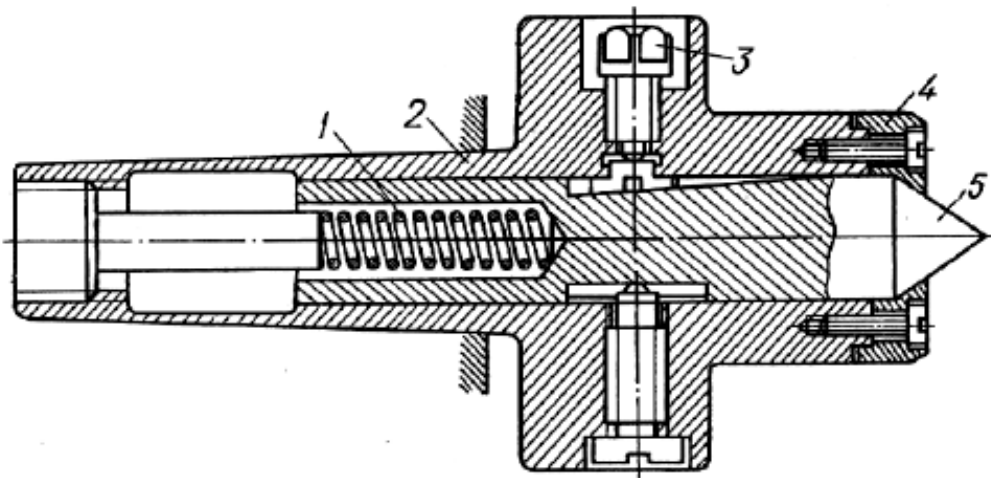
Плаваючий центр: 1 – пружина; 2 – корпус; 3 – гвинт; 4 – упор; 5 - центр
